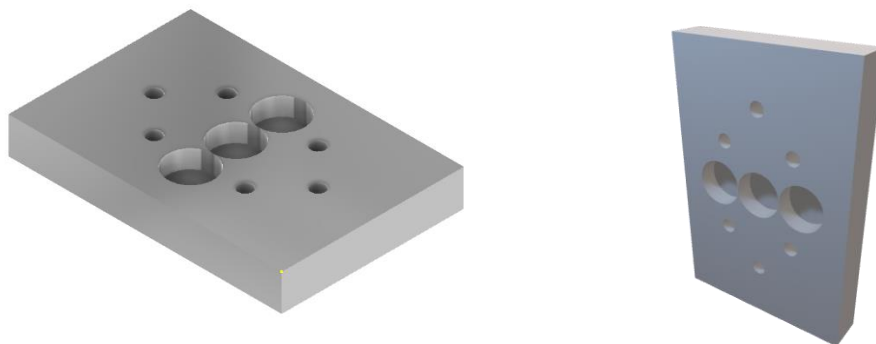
Τρισδιάστατη απεικόνιση αποστολής 29
